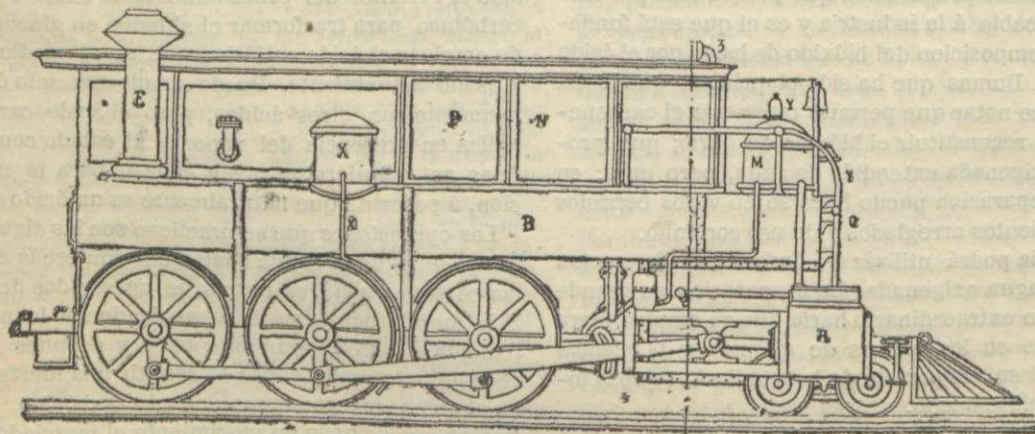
^a—Vista exterior de la locomotora Rothrock
